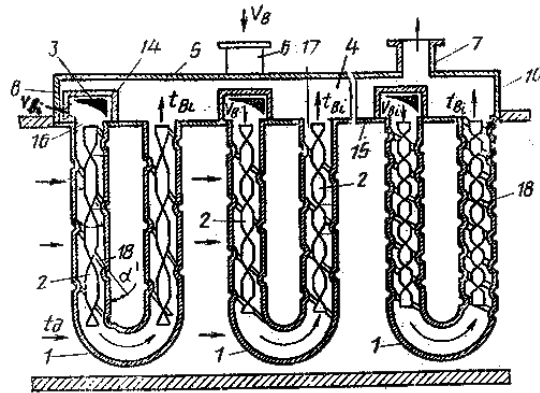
Рекуператор [29]: 1) U-образная труба; 2) закрученная вставка; 3) воздушный короб; 4) короб нагретого воздуха; 5) крышка; 6) подводный патрубок; 7) отводящий патрубок; 8, 9, 10, 11) боковые стенки; 12) разделительная стенка; 13) отверстия; 14) П-образная раздаточная труба; 15) распределительная пластина; 16, 17) впускное и выпускное отверстие; 18) многозаходные спиральные выступы
